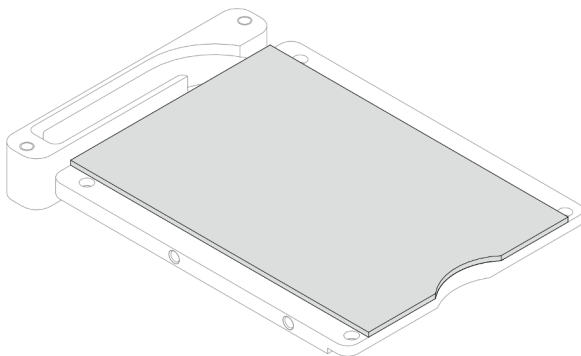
Installation d'une plaque de conduction dotée d'un tampon d'espace
